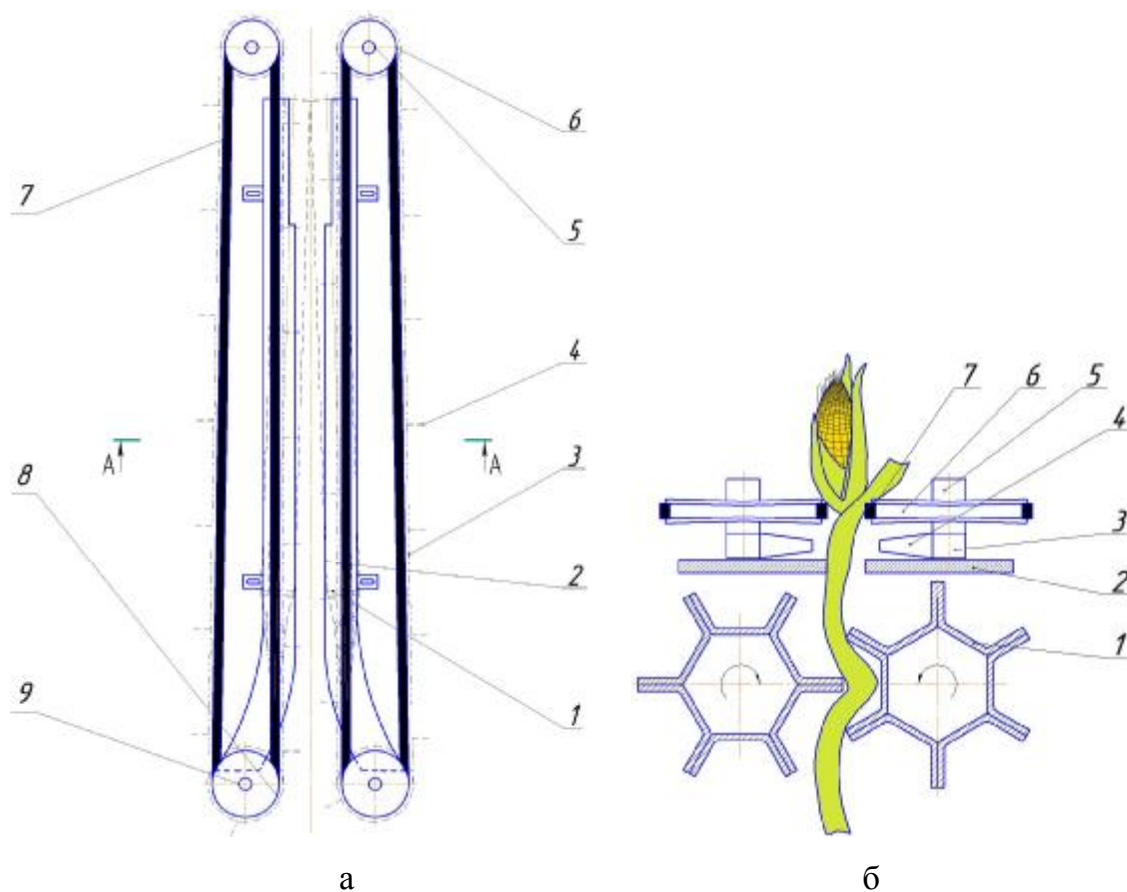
Початкоотделяющий аппарат: а – вид сверху; б – разрез А-А: 1 – протягивающий валец; 2 – початкоотделяющая пластина; 3 – подающая цепь; 4 – лапка цепи; 5 – вал; 6 – ведущий шкив; 7 – ремень; 8 – ведомый шкив; 9 – ось
